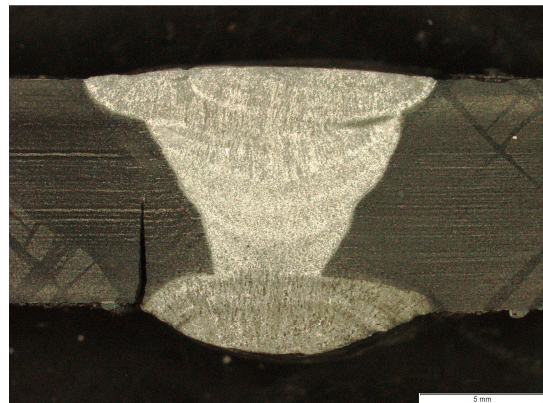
Probe G04-03, Schweißnaht FAT 112, Riss in der Schweißnaht
